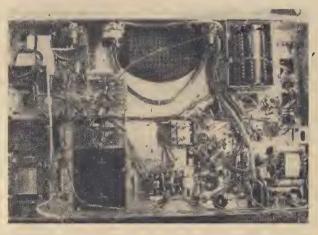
Unteransicht des Chassis, Blick in die Verdrahtung. Vgl. mit Bild 7
